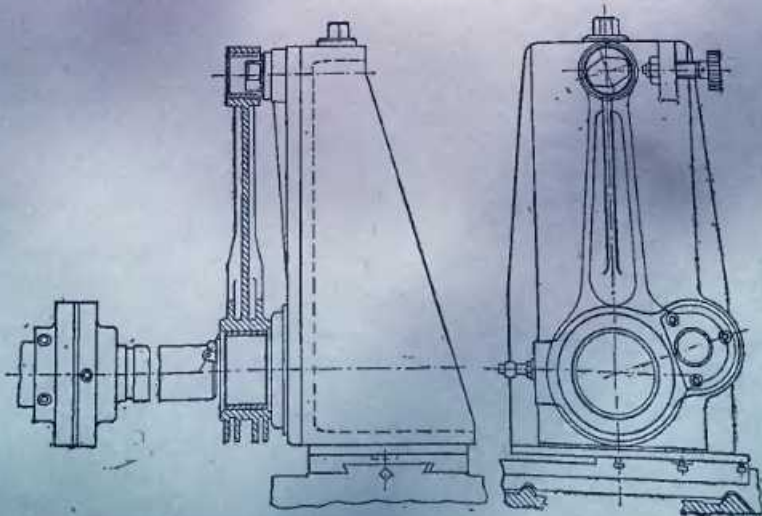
Приспособление ОЛ9649-001 для расточки вкладыша шатуна на токарном станке
